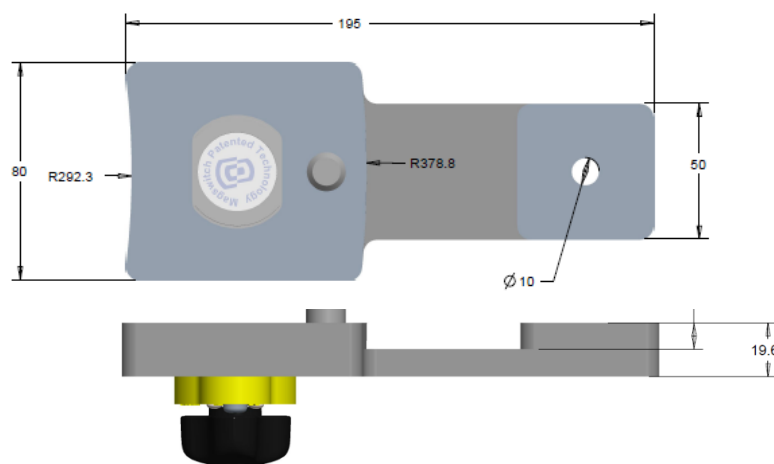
Varianta 4 - Modely prímerných prípravkov A, B a C
